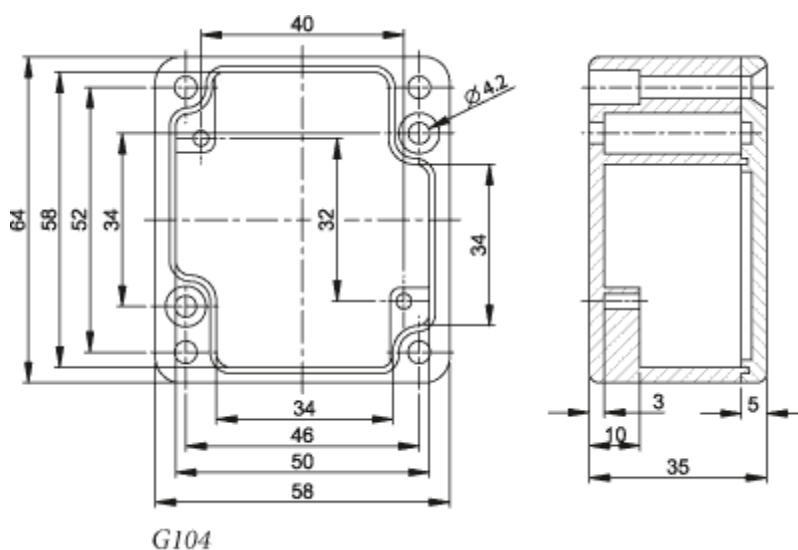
Конструкция корпуса GAINTA G104
